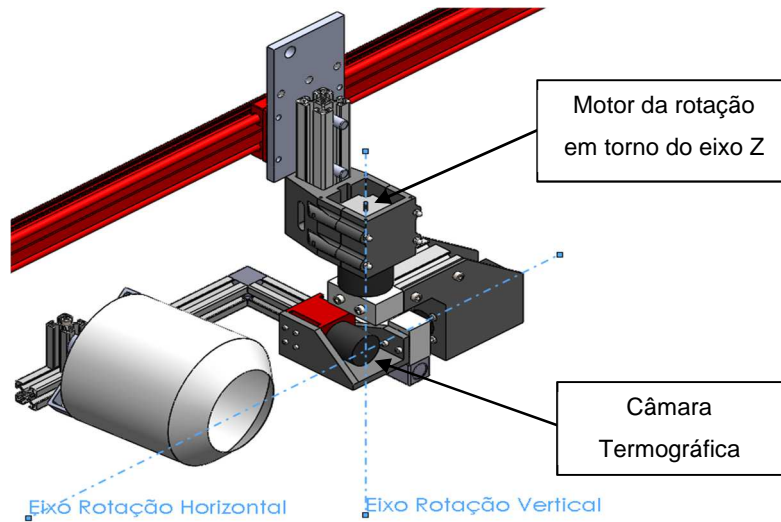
Vista isométrica frontal do módulo de termografia
